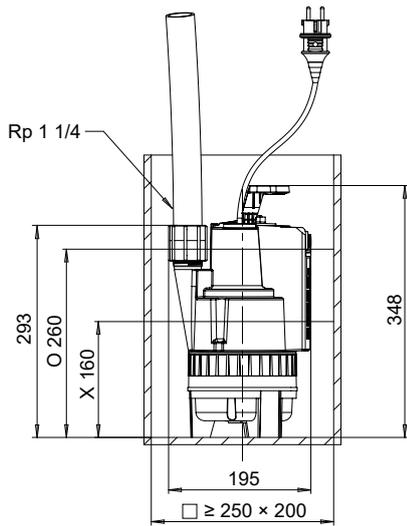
Dimensiones AmaDrainer 322 [mm]
